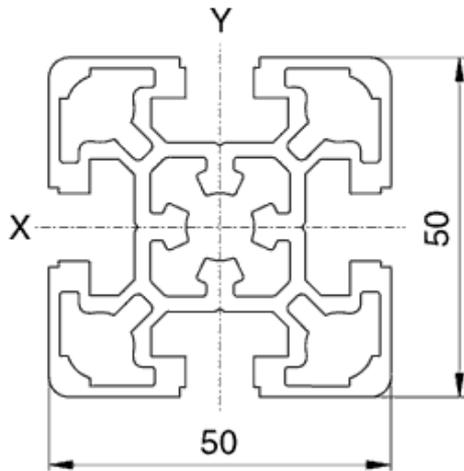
Querschnitt Bosch Rexroth Maschinenbauprofil
